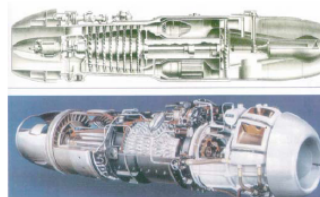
Первые реактивные двигатели боевых самолетов с осевыми компрессорами. Германия. 1944 г. [2]
